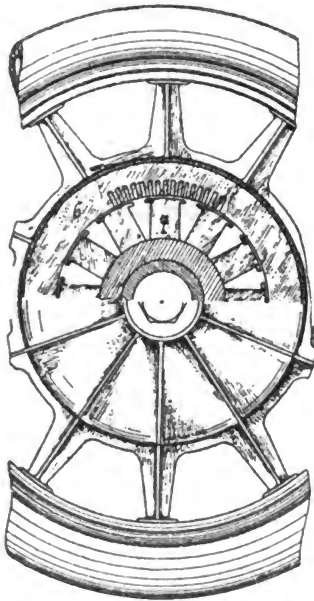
Ansicht des Elektromotors der Firma Jacob Lohner & Co.
